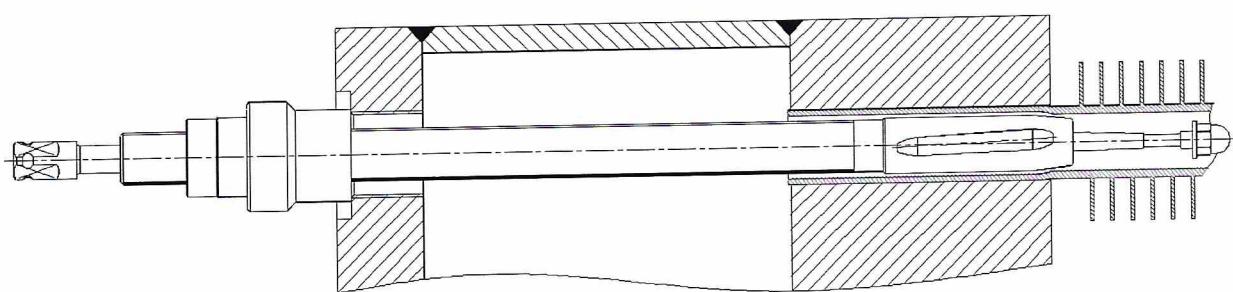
Удлиненная регулируемая вальцовка в сварной камере
